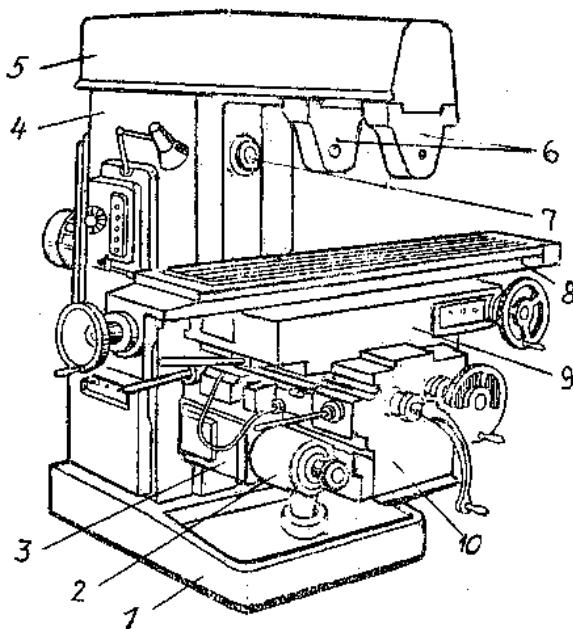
Общий вид горизонтально-фрезерного станка
